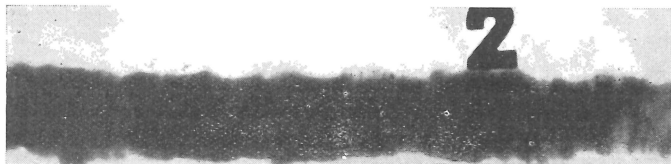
Radiographie d'une soudure en X (tôle de 18 mm) : soudure sans défaut, présentant une surépaisseur assez importante par rapport au métal voisin.
